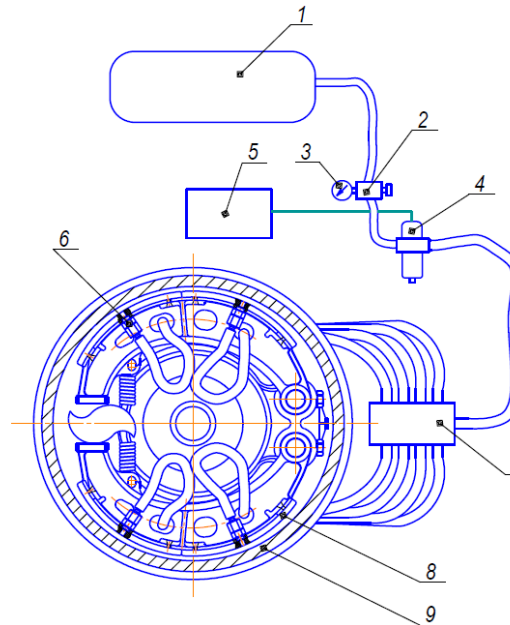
Схема СППВ экспериментального ТМ: 1 – ресивер; 2 – управляемый редуктор; 3 – манометр; 4 – электромагнитный клапан; 5 – конечный выключатель тормозного крана; 6 – щипцы; 7 – система тройников; 8 – тормозная колодка; 9 – тормозной барабан.
